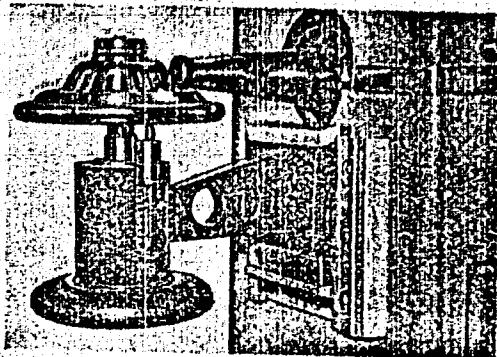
Приспособление для ультразвуковой сварки малых металлокерамических контактов.
